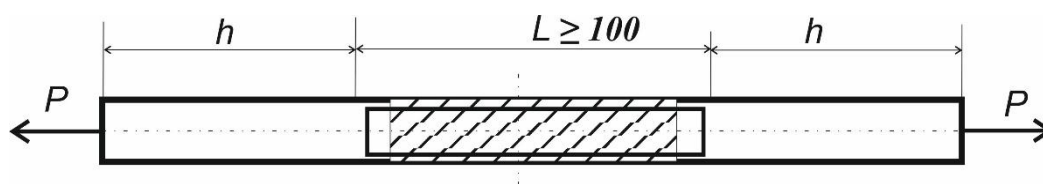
Эскиз заготовки для определения склонности к деформационному старению в ЗТВ реальных сварных соединений.
